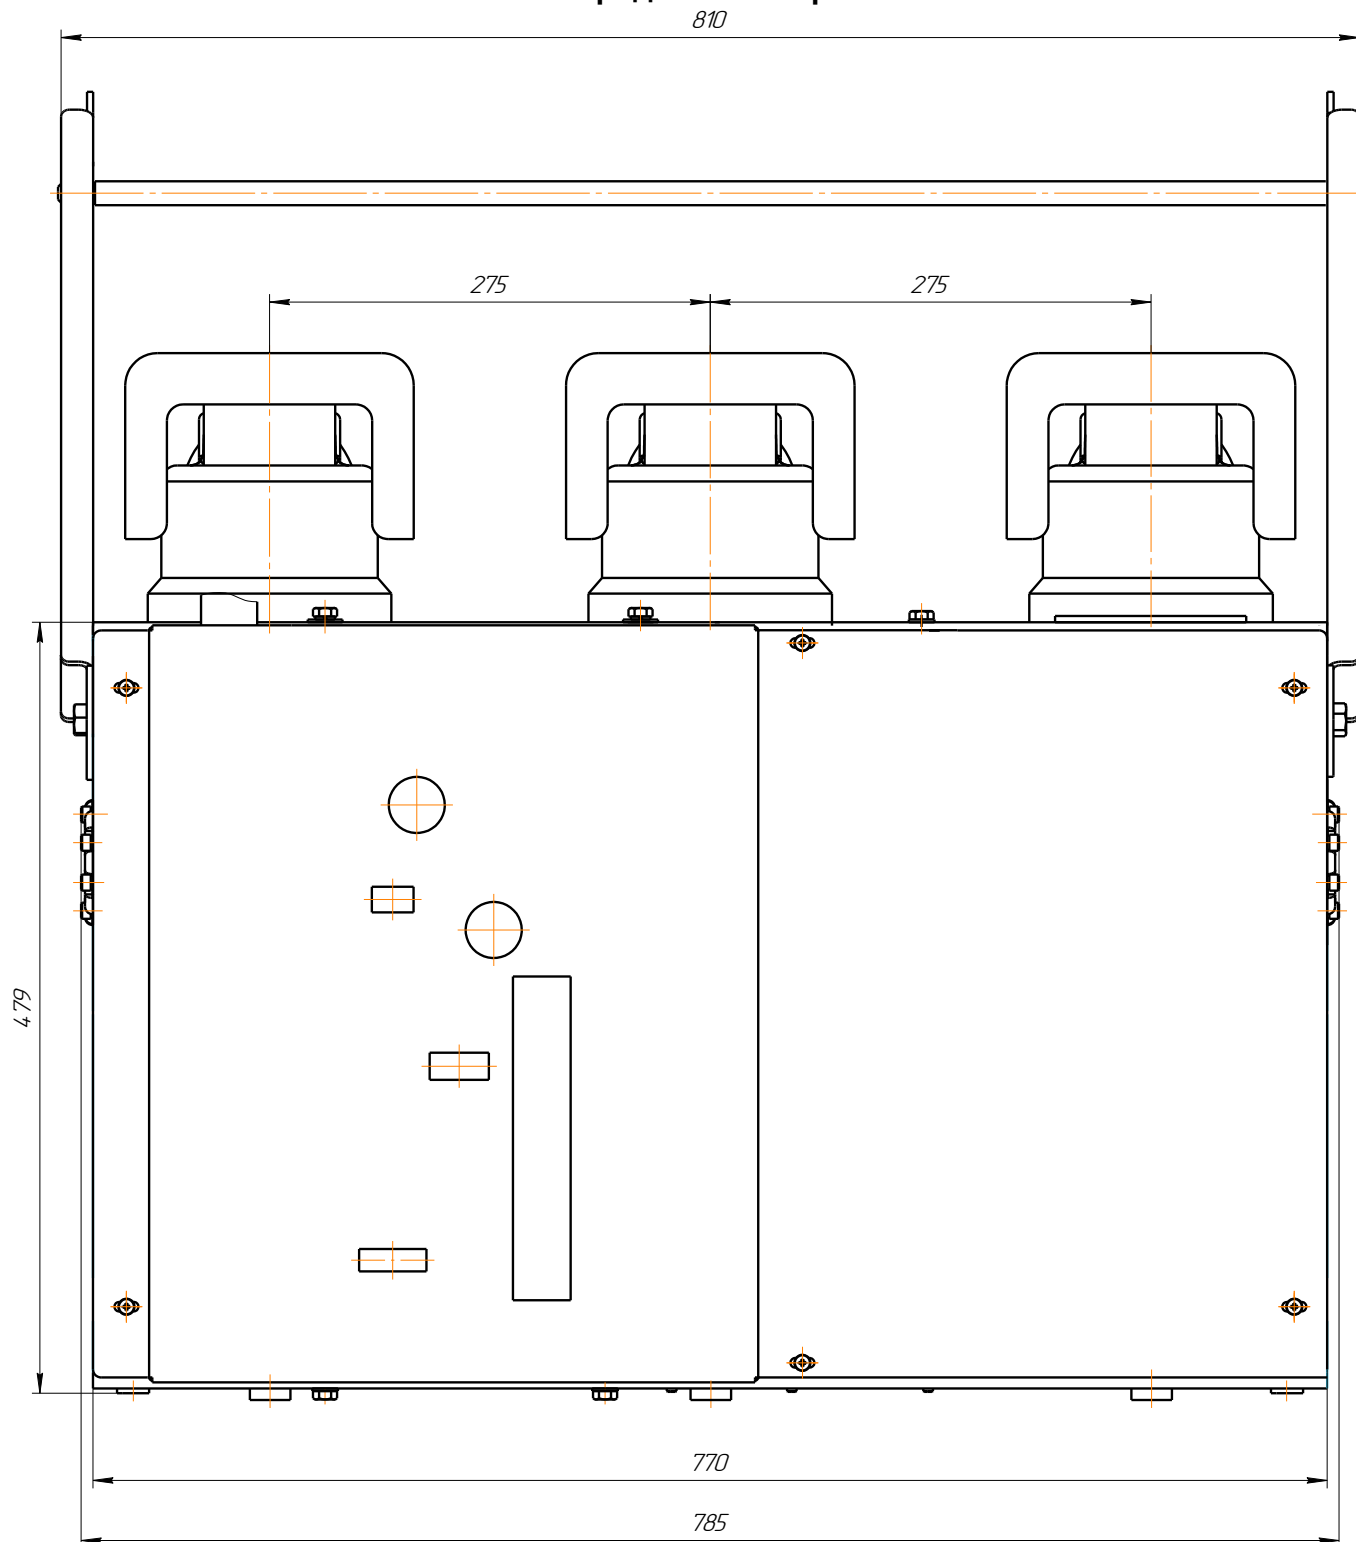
Габаритные и присоединительные размеры выключателя ВВУ-СЭЩ-10-40
